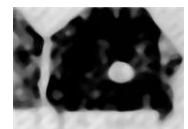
A. soldeertijd 1 seconde: geen soldering.
